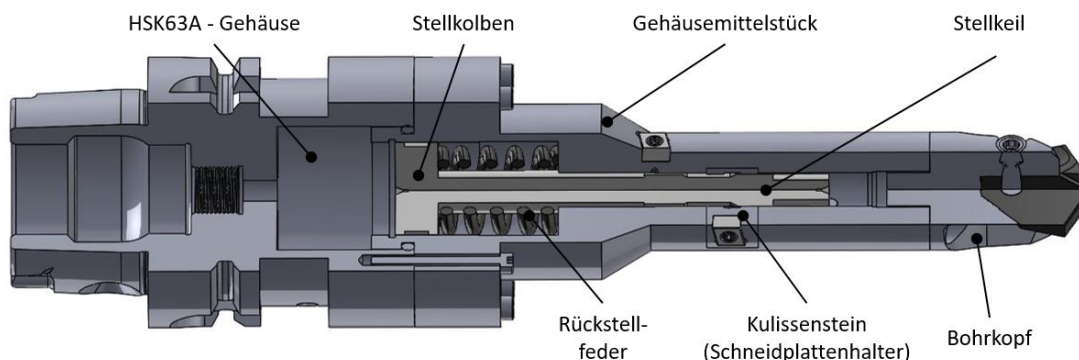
Pneumatisch/ hydraulisch arbeitender Werkzeugdemonstrator
